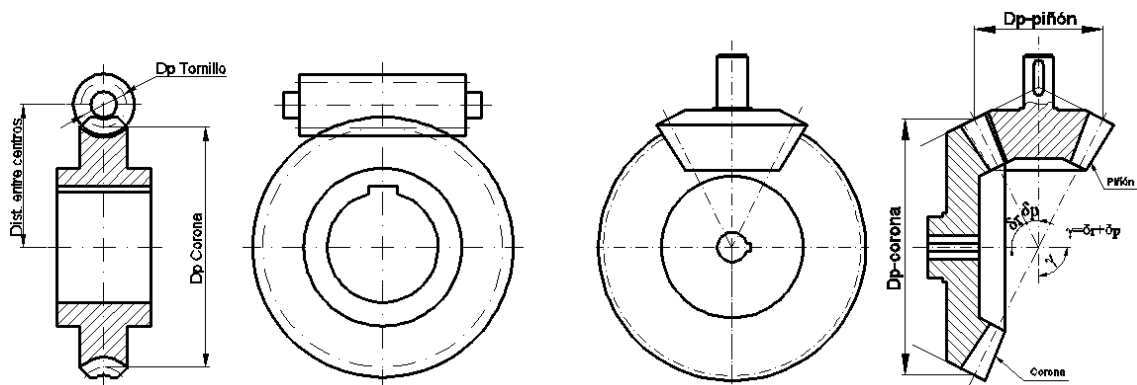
Representación de tornillo sin fin y par de engranajes cónicos.
